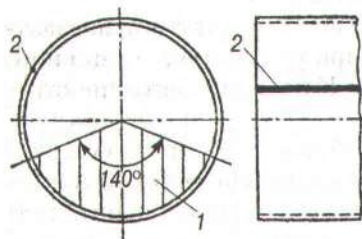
Розташування поздовжніх швів у горизонтальній посудині: 1 — зона, в якій зварні шви не розташовуються; 2 — зварний шов
